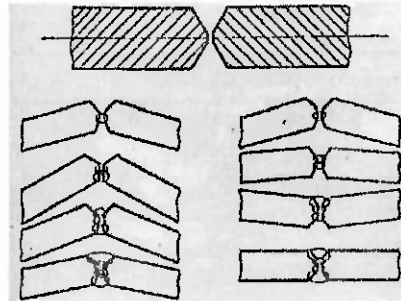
Sequência de soldagem do chanfro simétrico [7].
